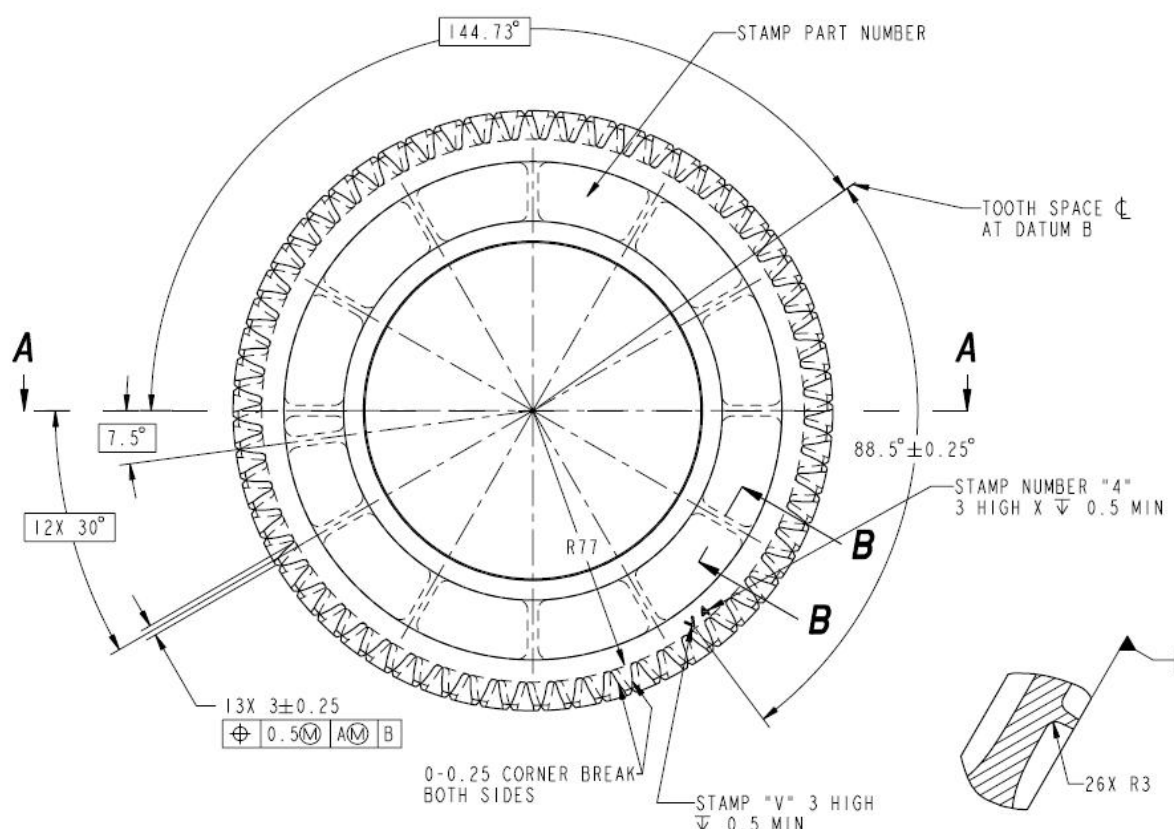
Plano de fabricación del frente del engranaje R504614
